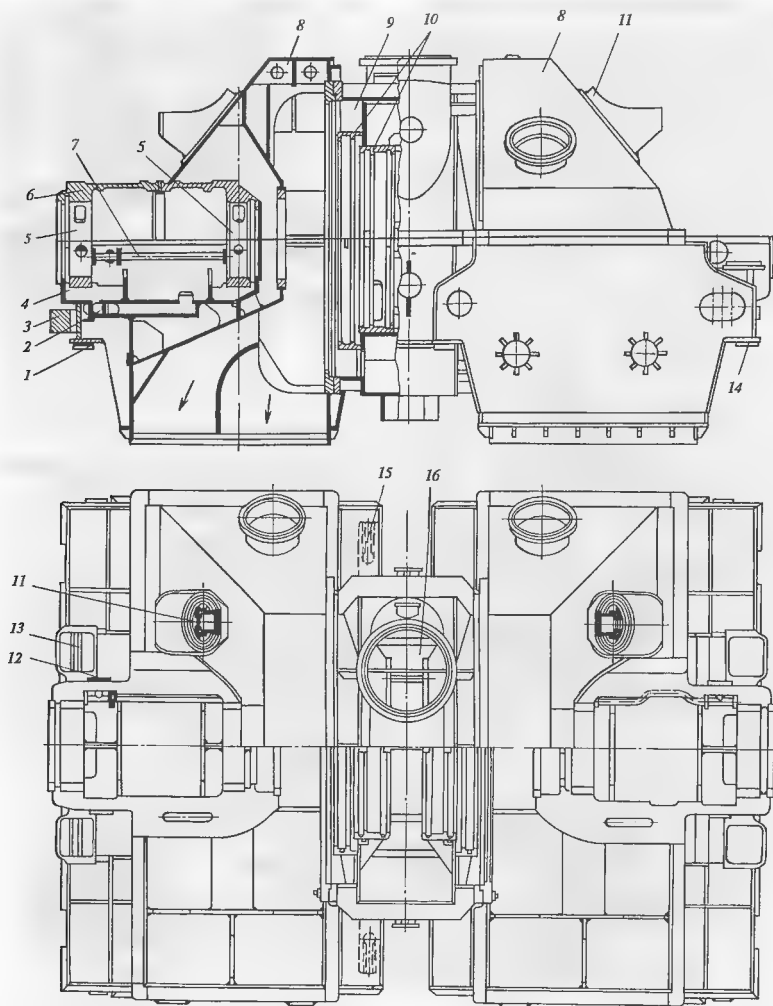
Конструкция одностенного корпуса ЦНД
